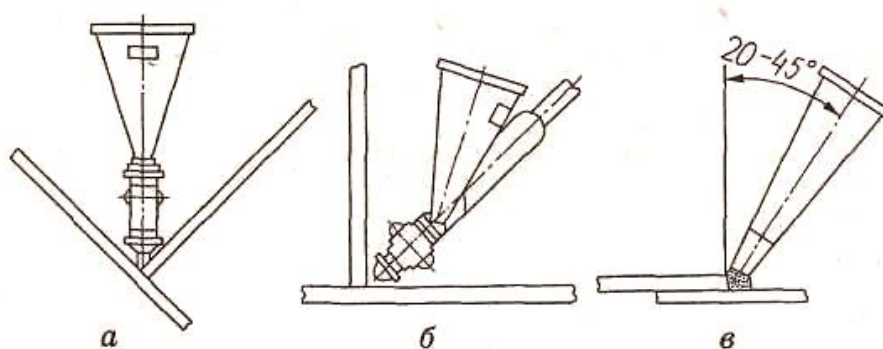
Схема полуавтоматической сварки под флюсом:
